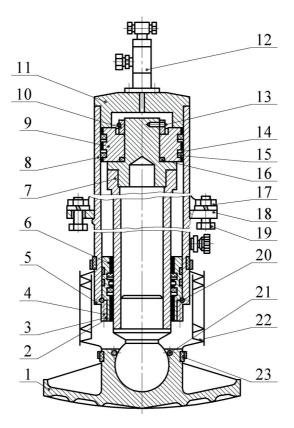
Домкрат гидравлический (аутригер): 1 – опорная плита; 2 – грязесьемник; 3 – конус; 4 – крышка; 5 – болт; 6 – крышка; 7 – шток; 8 – цилиндр; 9 – поршень; 10 – гайка; 11 – приварная крышка; 12 – гидрозамок; 13 – стопорное кольцо; 14 – защитное кольцо; 15 – резиновая манжета; 16 – кольцо; 17 – гайка; 18 – фланец; 19 – болт; 20 и 21 – кольцо; 22 – защитный кожух; 23 – лента
